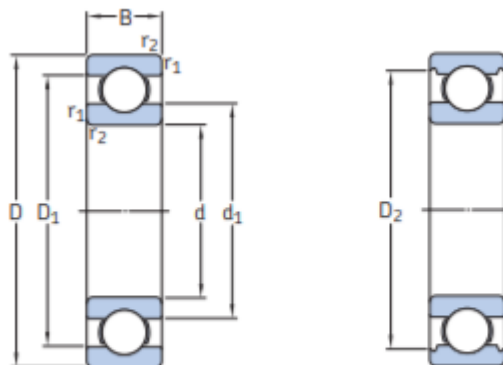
Dimensiones de rodamiento de una hilera de bolas SKF
